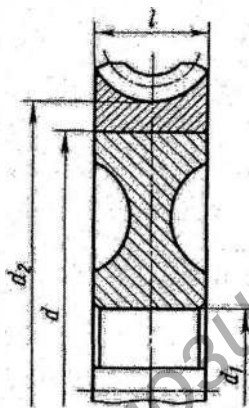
Червячное колесо с напрессованным зубчатым венцом [9, с. 46]
